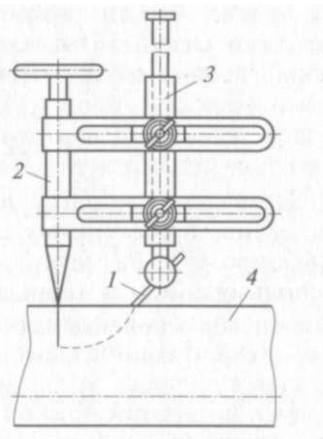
Универсальный циркуль для разметки отверстий:
